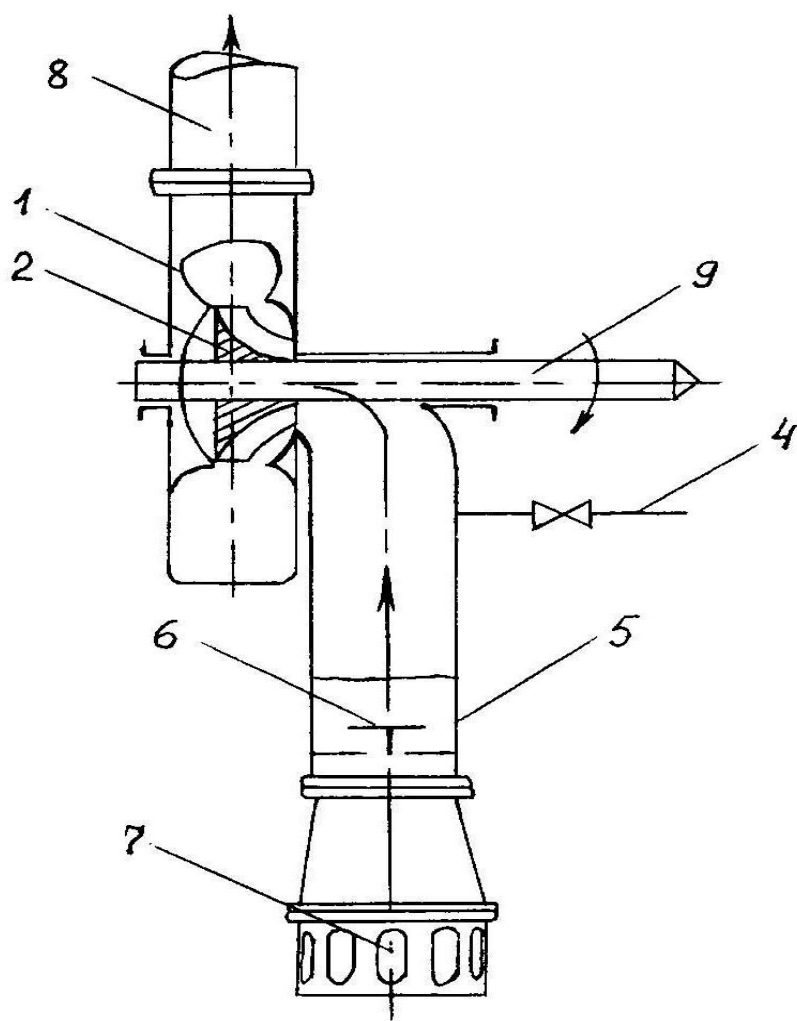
Схема центробежного насоса: 1 – корпус; 2 – рабочее колесо; 3 – лопатки; 4 – линия для залива насоса перед пуском; 5 – всасывающий патрубок; 6 – обратный клапан; 7 – фильтр; 8 – нагнетательный трубопровод; 9 – вал;
